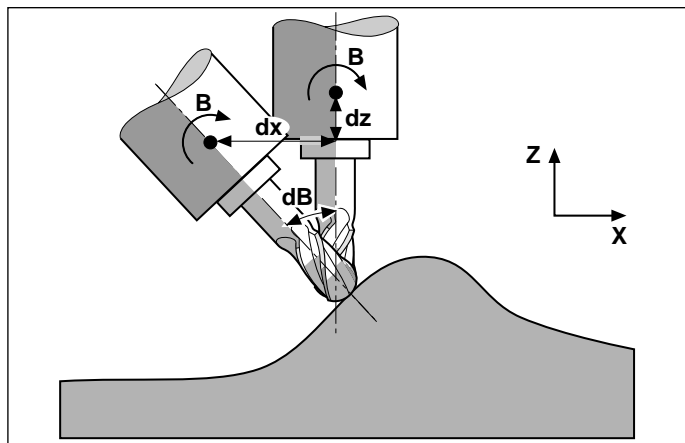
Versatz des Werkzeug-Bezugspunktes beim Schwenken des Werkzeugs
